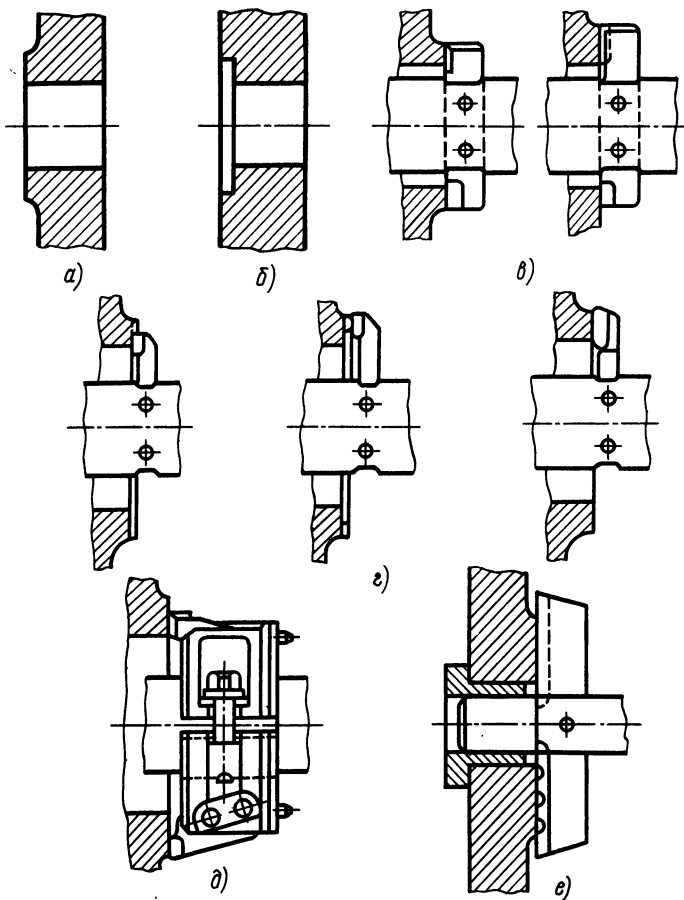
Виды торцовых поверхностей и способы их обработки с осевой подачей инструмента:
